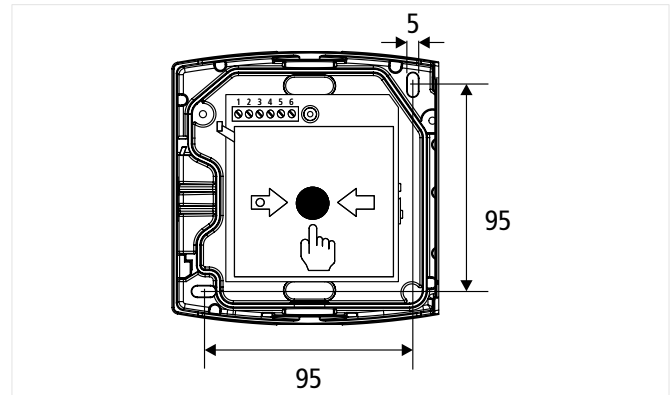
Abmessungen für Montagelöcher (Angaben in mm)
